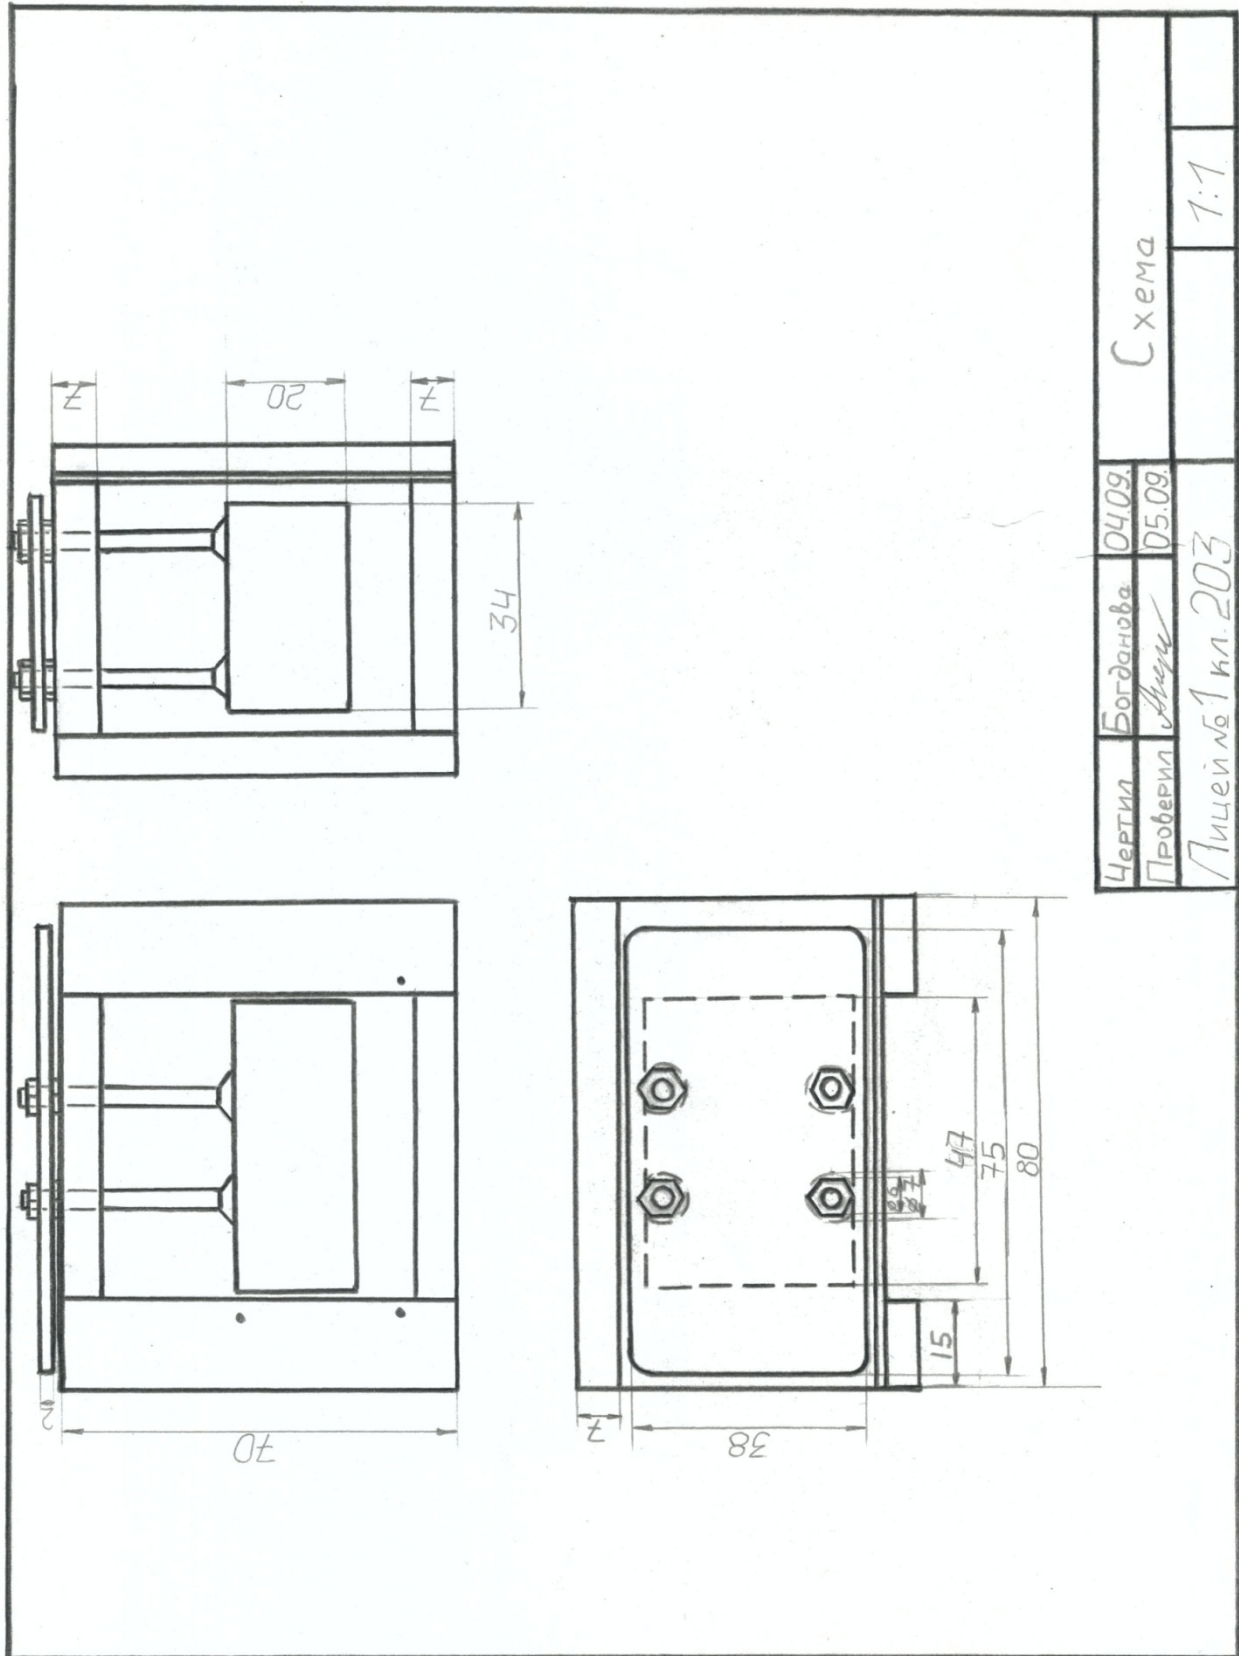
Схема установки с указанием размеров (вид спереди, вид сверху, вид сбоку)
